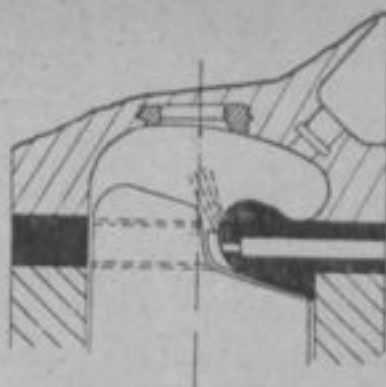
Головка двухтактного швейцарского двигателя с «промежуточной» головкой
